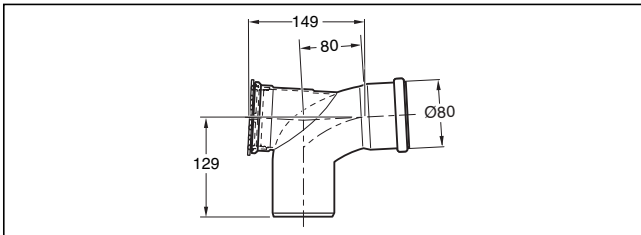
Bogen mit Prüföffnung lang (Maße in mm)
